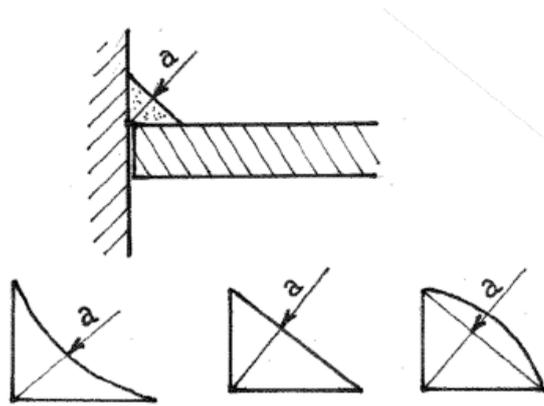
Épaisseur a d'un joint de soudure d'angle.
